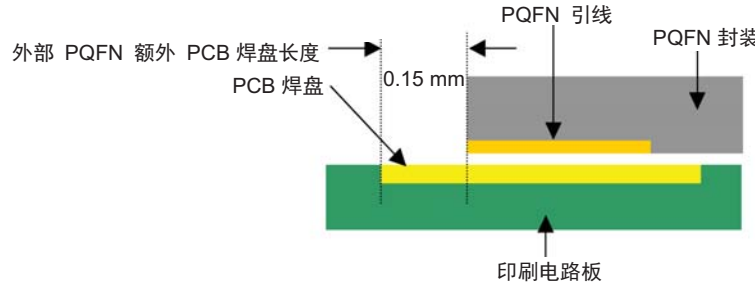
封装引脚和推荐 PCB 焊盘的横截面
